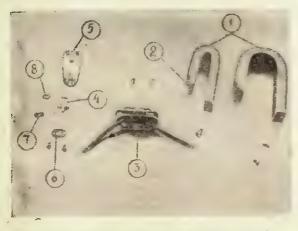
Детали рекордера т. Успенского: 1 — магниты индуктора (цифрой 2 показана выемка для крепления детали 3); 2—модуляционная часть с полюсными наконечниками; 3—якорь; 4 — планка крепления якоря; 5 — шайба крепления якоря; 6 — демпфирующее кольцо
